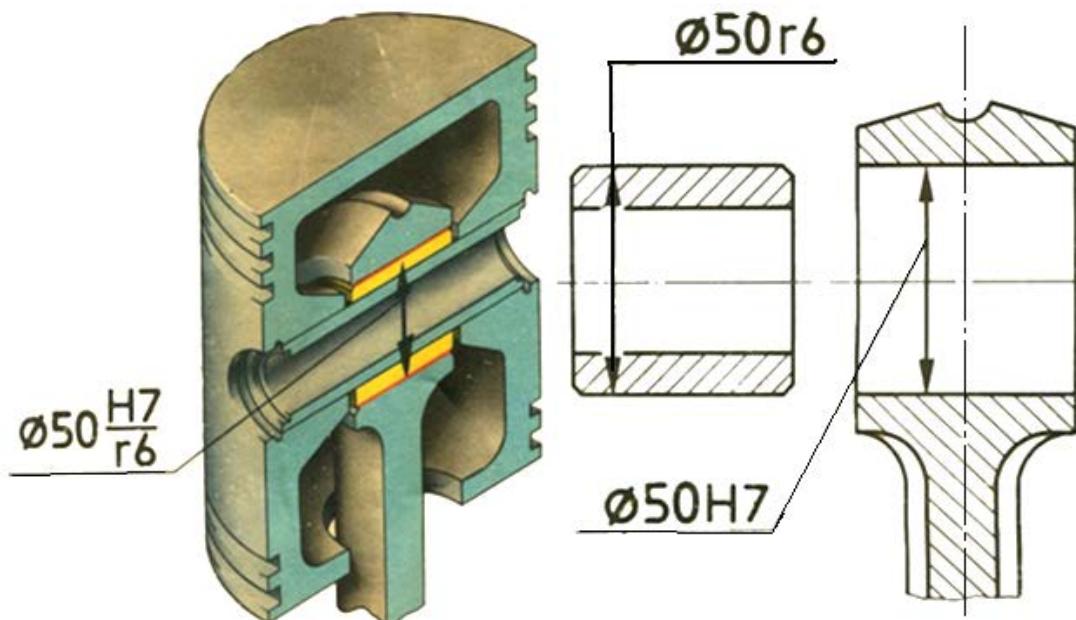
Втулка в головке шатуна тракторного двигателя
